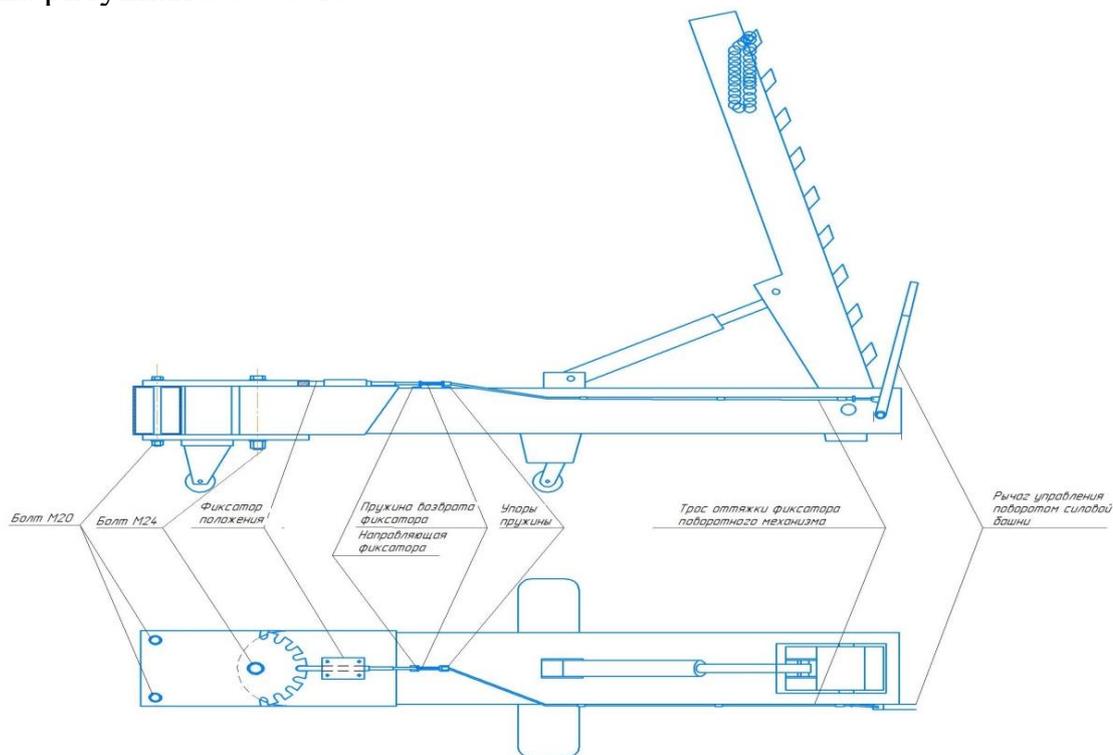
Принципиальная схема устройства поворотного механизма силовой башни stapеля с ручным управлением
